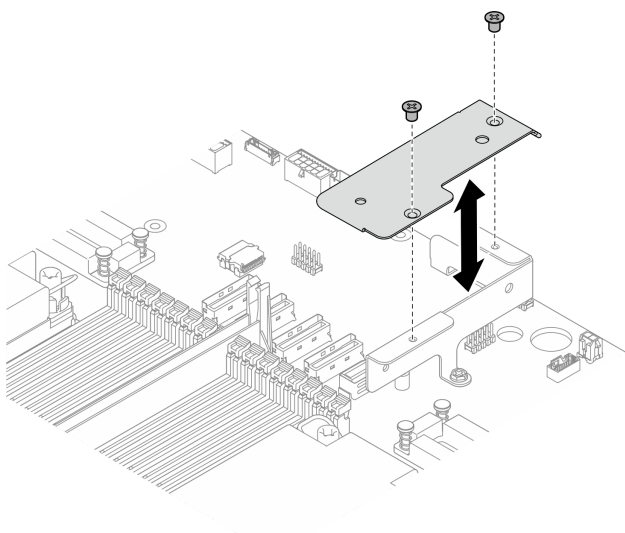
Extracción e instalación de la cubierta central de la guía de cables
